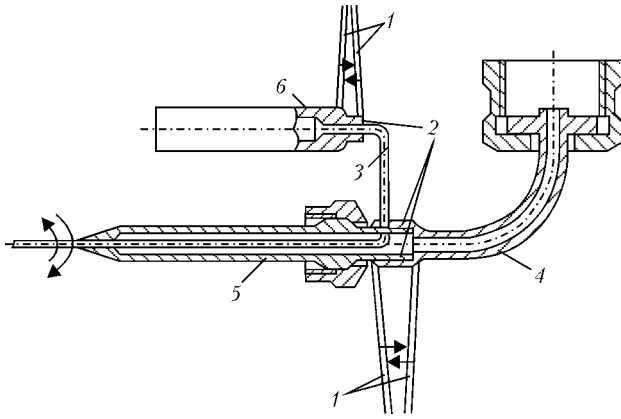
Схема пайки узла медицинского инструмента: 1 — колеблющийся электронный пучок; 2 — цилиндр; 3 — игла; 4 — патрубок; 5 — рабочий цилиндр; 6 — припой
